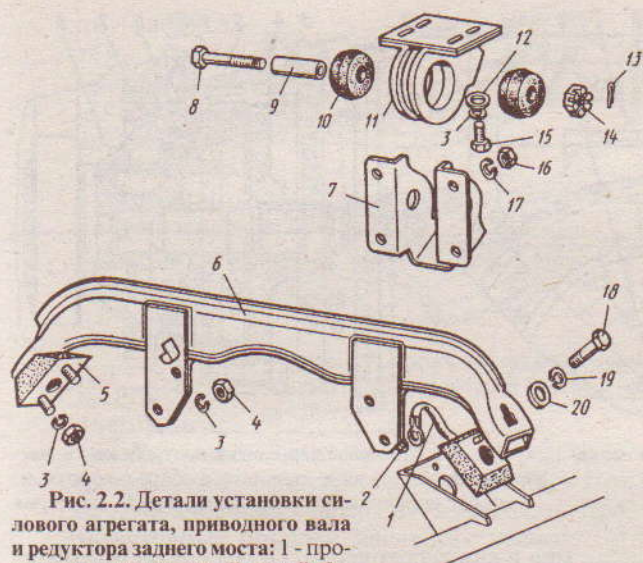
Детали установки силового агрегата, приводного вала и редуктора заднего моста: 1 - провод от двигателя на "массу"; 2 - шайба 8; 3 - шайба 8Л; 4 - гайка М8; 5 - подушка передней опоры двигателя; 6 - поперечина передней опоры силового агрегата; 7 - кронштейн крепления редуктора заднего моста; 8 - болт 2М12; 9 - втулка распорная; 10 - амортизатор задней опоры силового агрегата; 11 - опора редуктора заднего моста; 12 - шайба 8; 13 - шплинт 3,2x32; 14 - гайка М12; 15 - болт М8; 16 - гайка М10; 17 - шайба 10; 18 - болт; 19 - шайба 12; 20 - шайба 12
